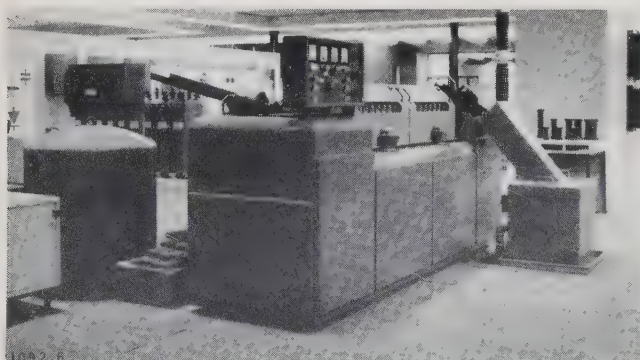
Durchlauferhitzer zum Erwärmen von Schmiedestücken.
